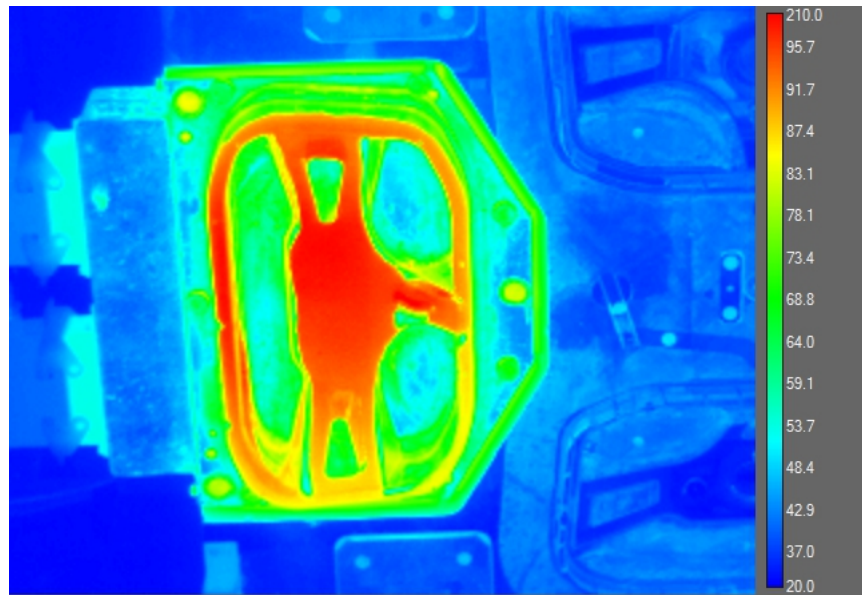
Profil thermique de la partie avant de la pièce après estampage
